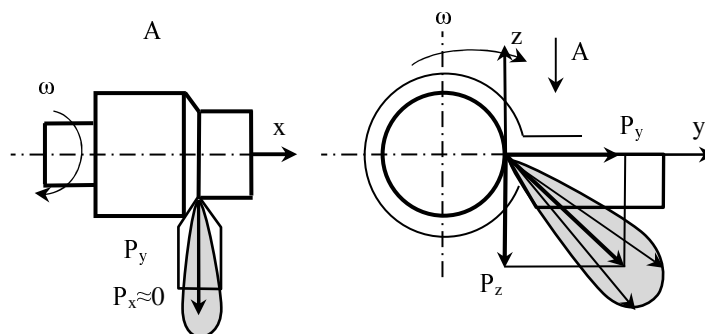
Схема токарної обробки деталі, що характеризується випадковими змінами сили різання
